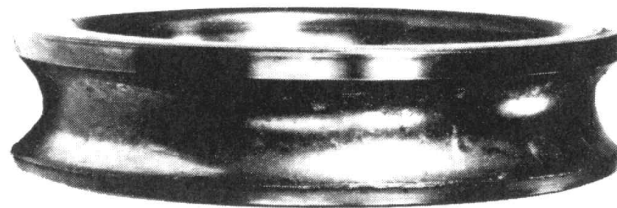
과도한 스트레스에 의한 Spalling
